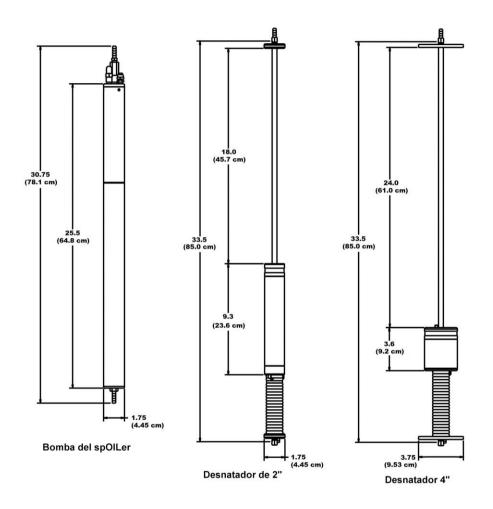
Dimensiones del SpOlLer y Desnatador
